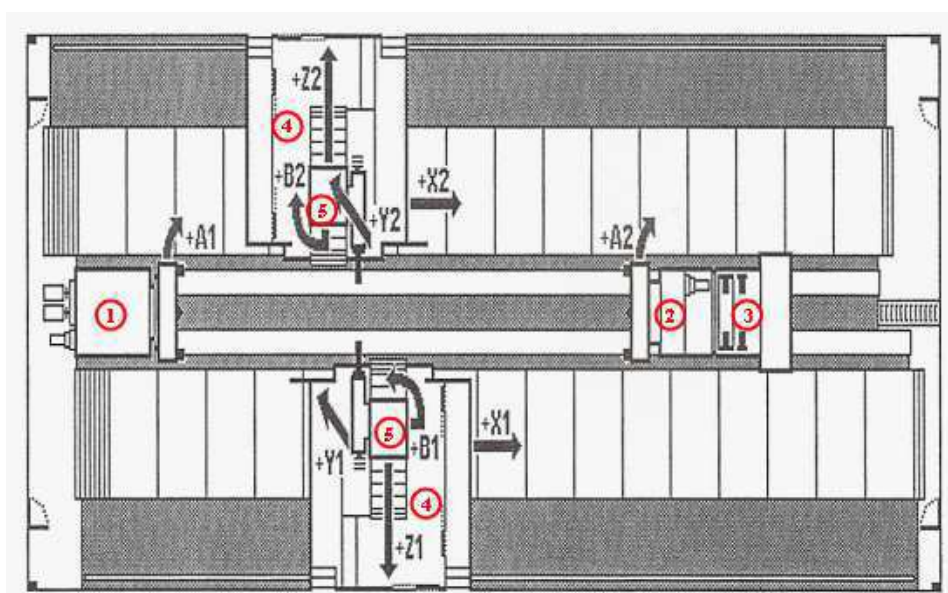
Speciální NC stroj typu PC 6 [8]
